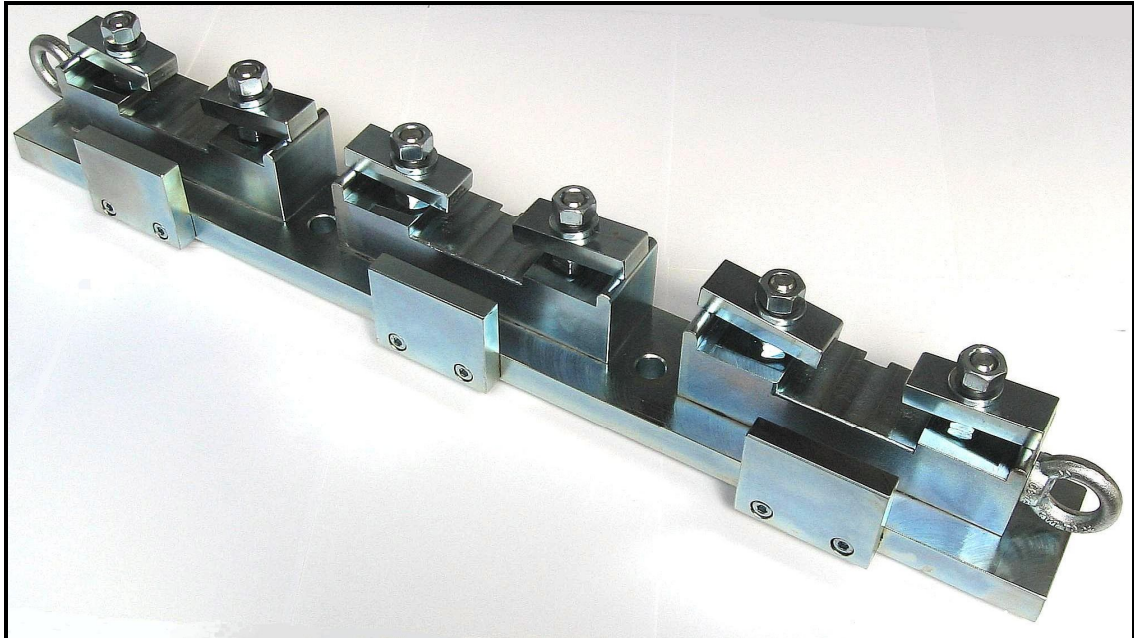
Upnutí přípravku na stůl frézky – první operace
